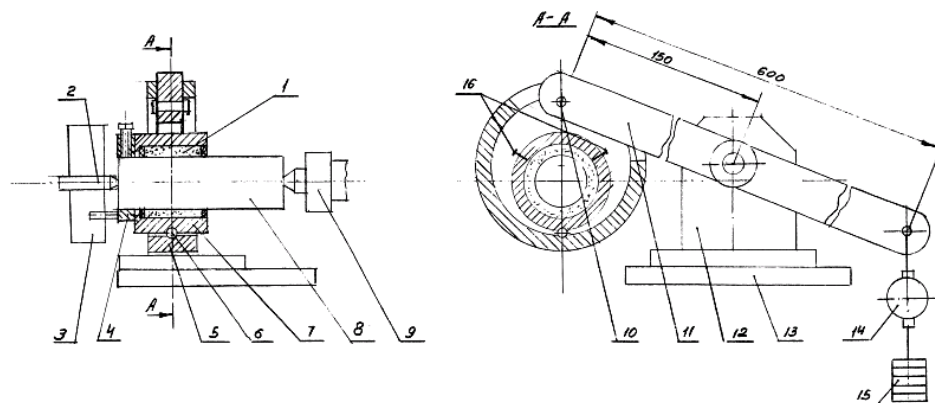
Схема нагрузочного устройства: 1 – пористый образец; 2 – центр; 3 – патрон токарный; 4 – хомут поводковый; 5 – кольцо натяжное; 6 – опора
